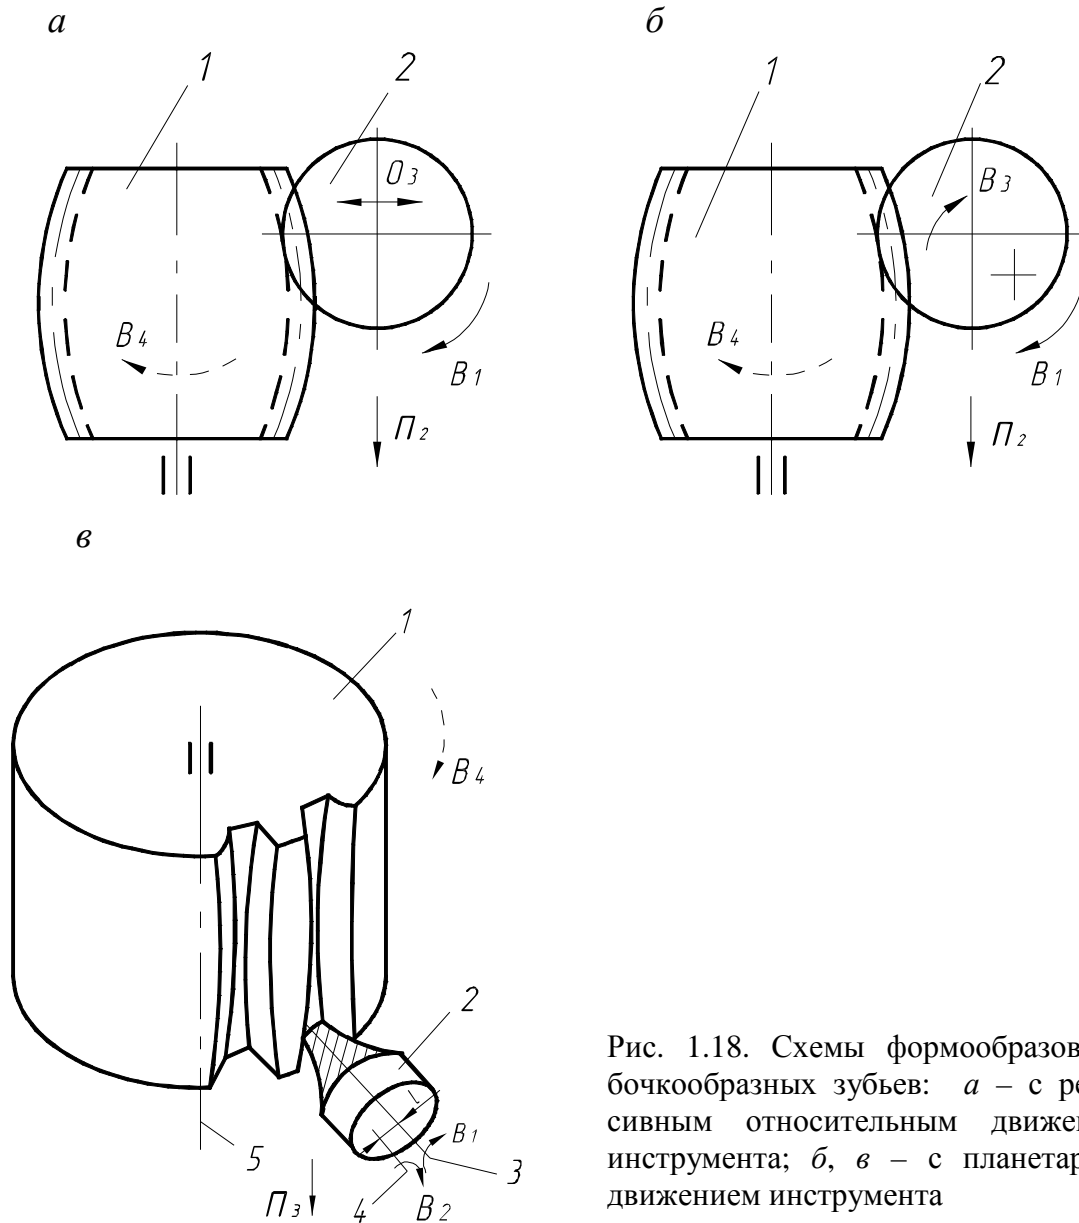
Схемы формообразования бочкообразных зубьев: а – с реверсивным относительным движением инструмента; б, в – с планетарным движением инструмента
